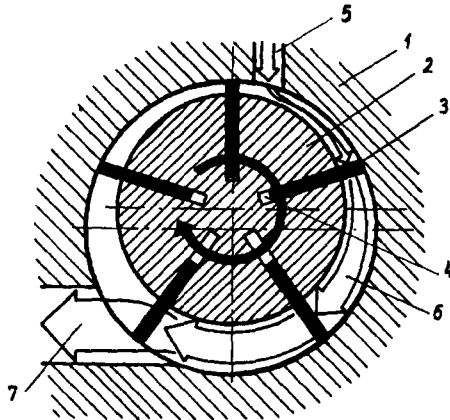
Rotačný pneumatický motor s radiálnymi membránovými piestami
